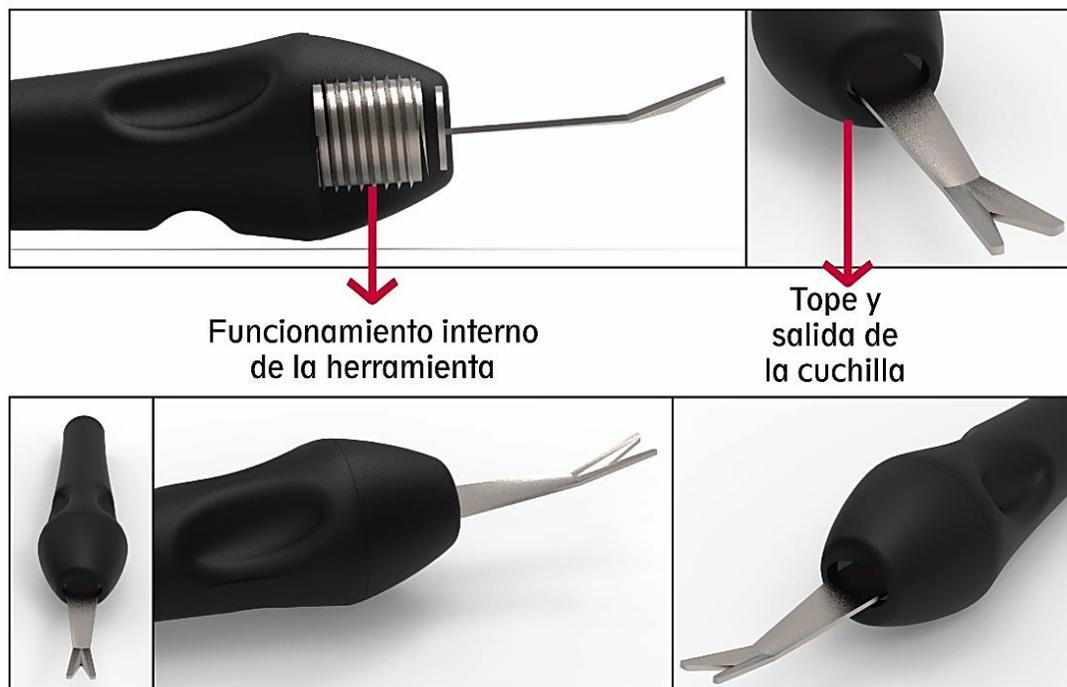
Parte 2 de diseño de detalles. Fuente: Elaboración propia
